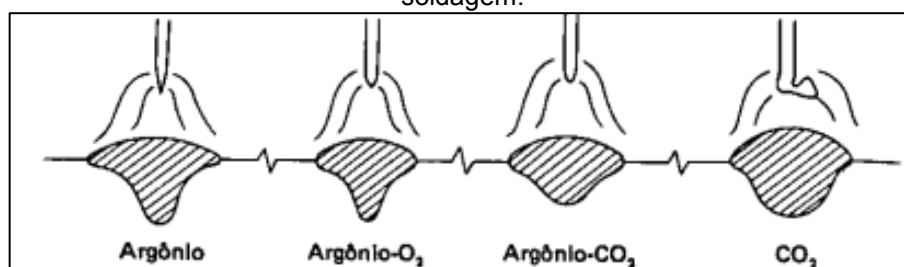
Representação esquemática do processo de soldagem MIG/MAG.
